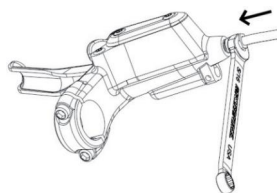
Utilisez une clé plate de 8 mm pour desserrer/serrer la vis de fixation du tuyau d'huile
